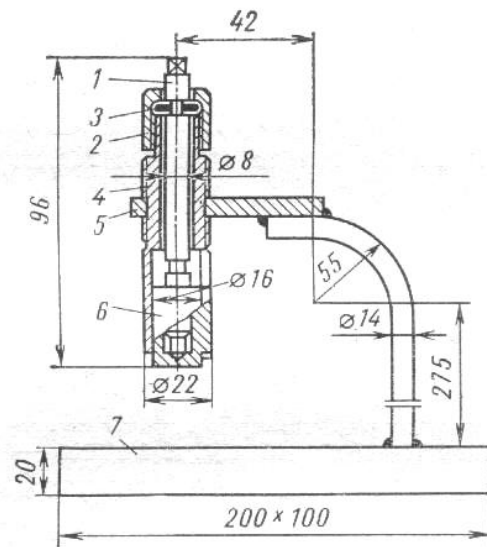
Мікропрес для раздавлювання гранул: 1 – гвинт; 2 – накидна гайка; 3 – “сухар”; 4 – корпус; 5 – фланець; 6 – поршень; 7 – станина.
